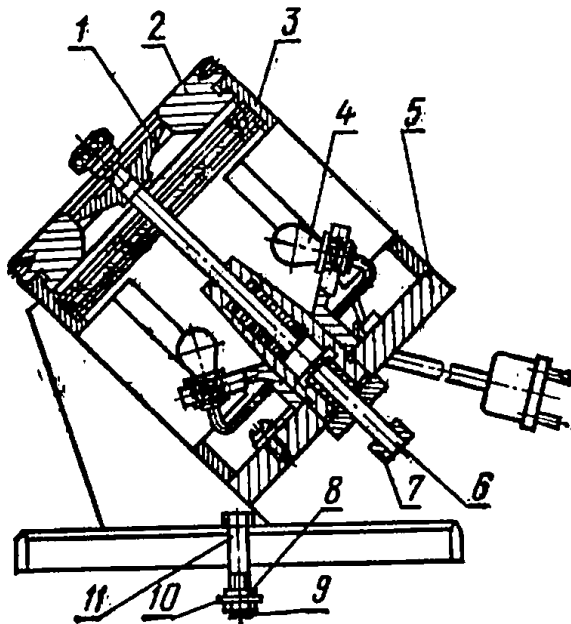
Приспособление для проверки наружного диаметра пальцев:
